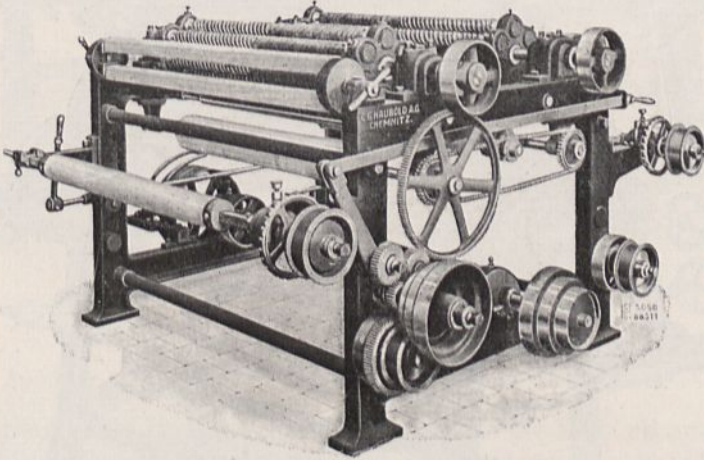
Appretur-Brechmaschine mit Spiralmessern.
